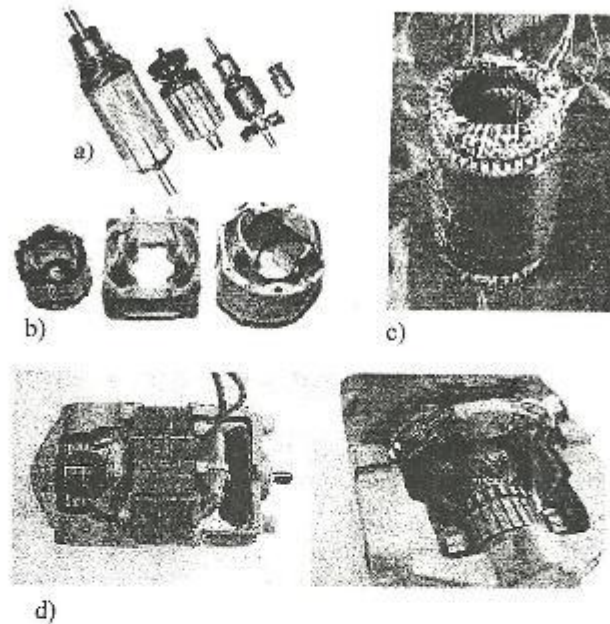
Partes componentes de un motor universal. a) Diferentes tipos de rotores. b) Estatores de polos salientes. c) Estator ranurado. d) Motor universal de polos salientes
